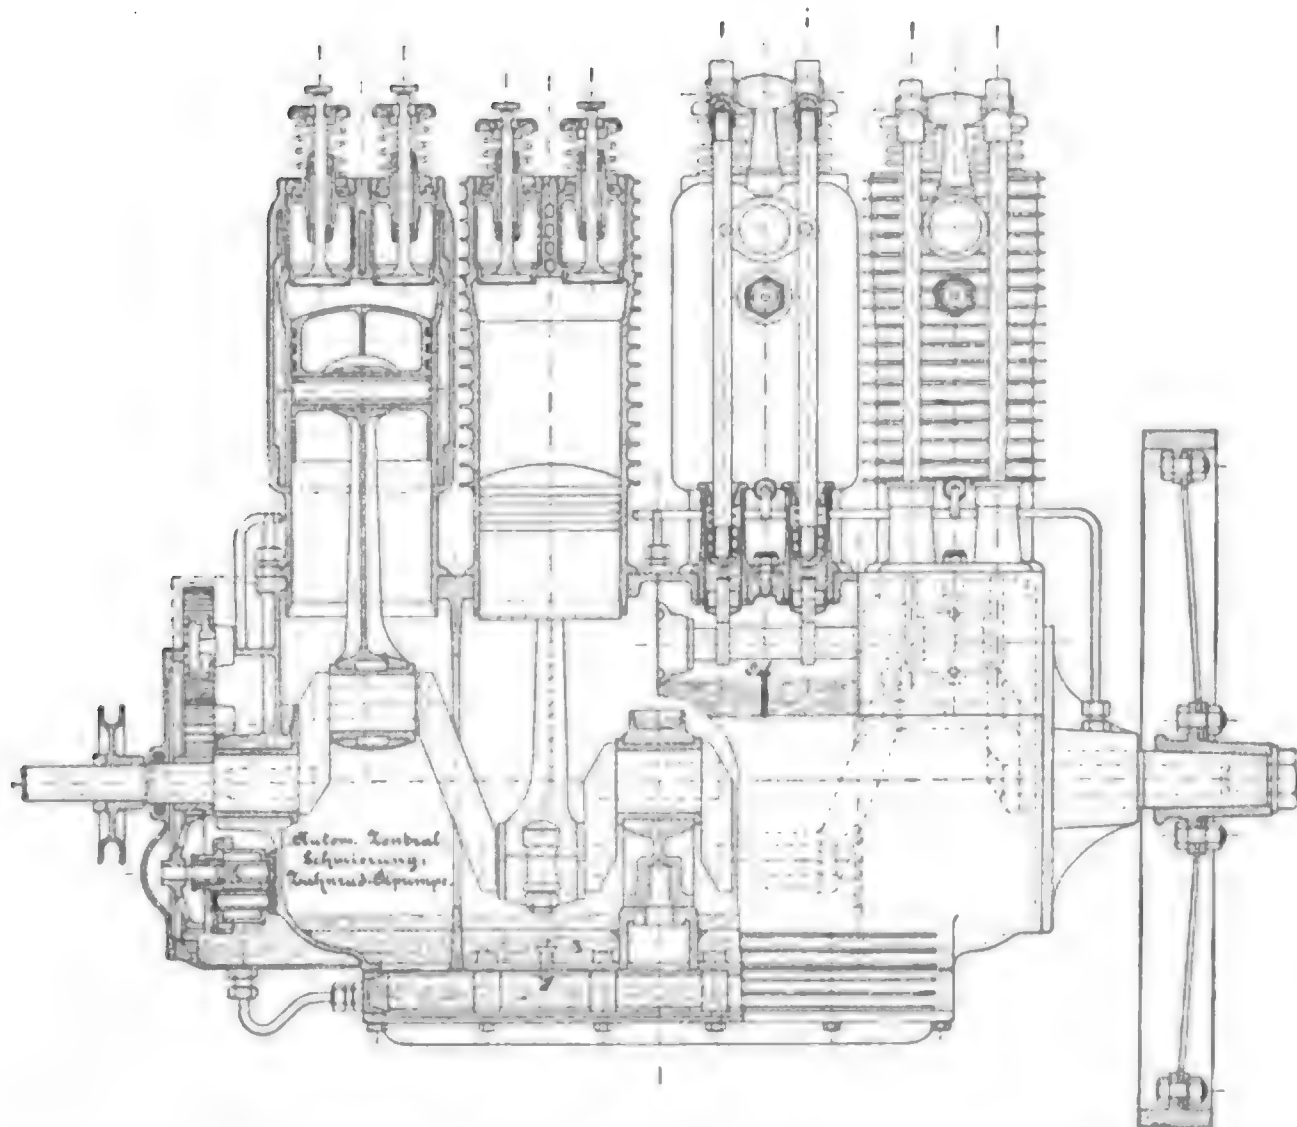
Zeichnung des Flugmotors von Escher & Co. mit stehenden Zylindern.
